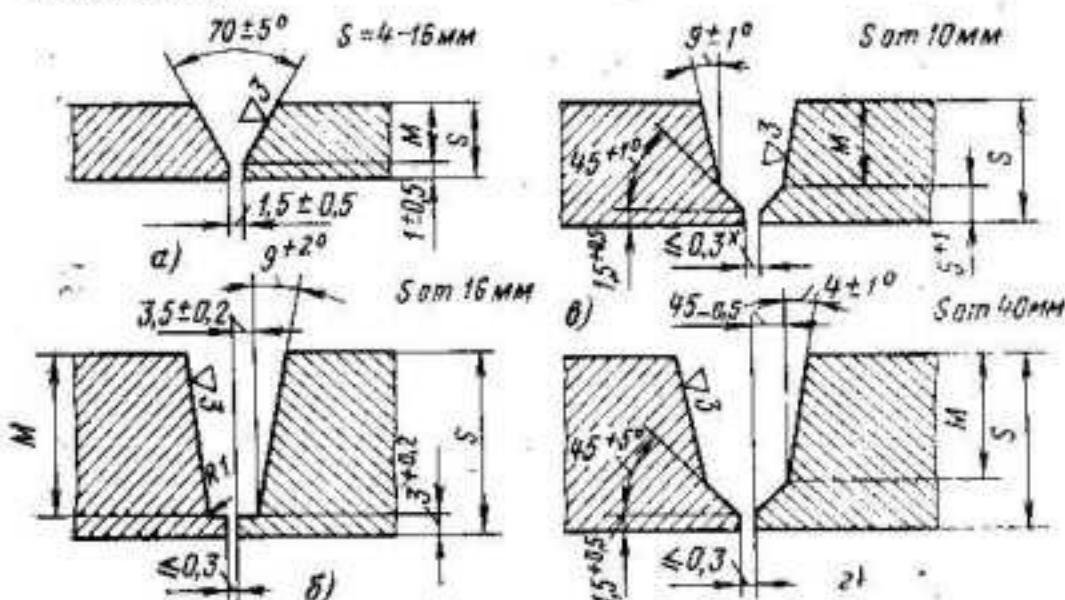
Подготовка кромок труб под сварку.
